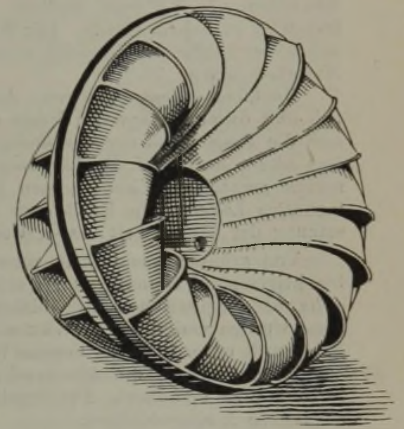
Ansicht des 50-t-Turbinen-Laufrades nach der Entnahme aus der Form.
